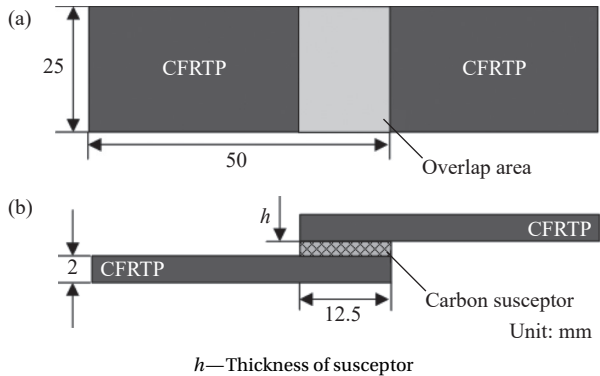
CF/PEEK 感应焊接试样尺寸: (a) 俯视图; (b) 正视图
